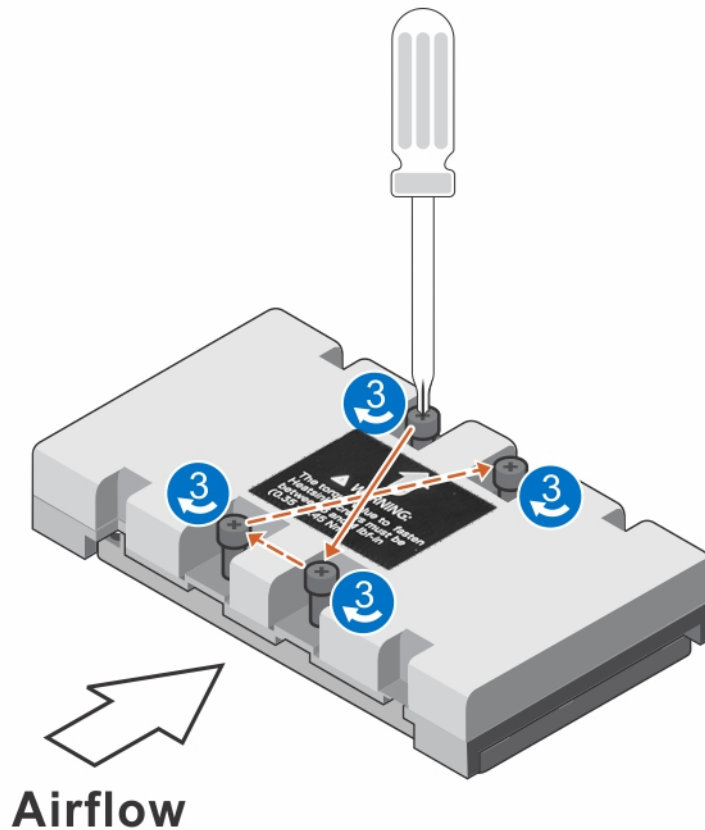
Installieren der SXM2-GPU-Kühlkörperschrauben
